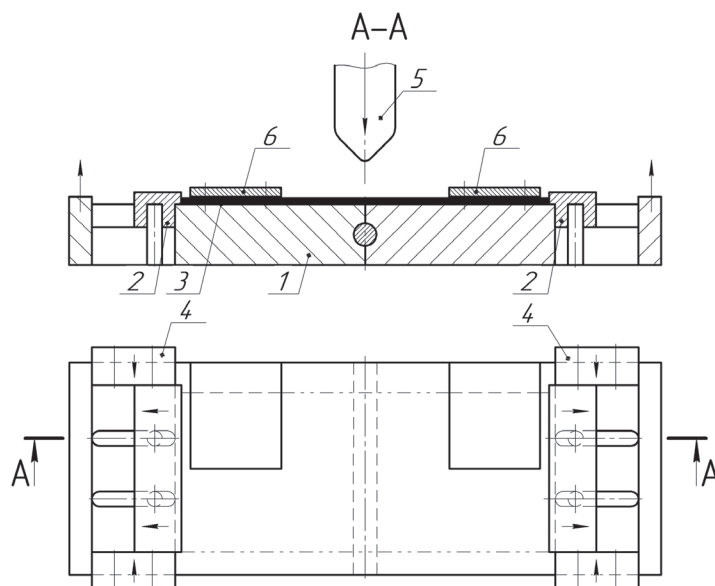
Схема штампа для гибки высокопрочных сталей с боковыми поджимами: 1 – шарнирная матрица; 2 – упор; 3 – заготовка; 4 – боковой поджим; 5 – пуансон; 6 – ограничитель
